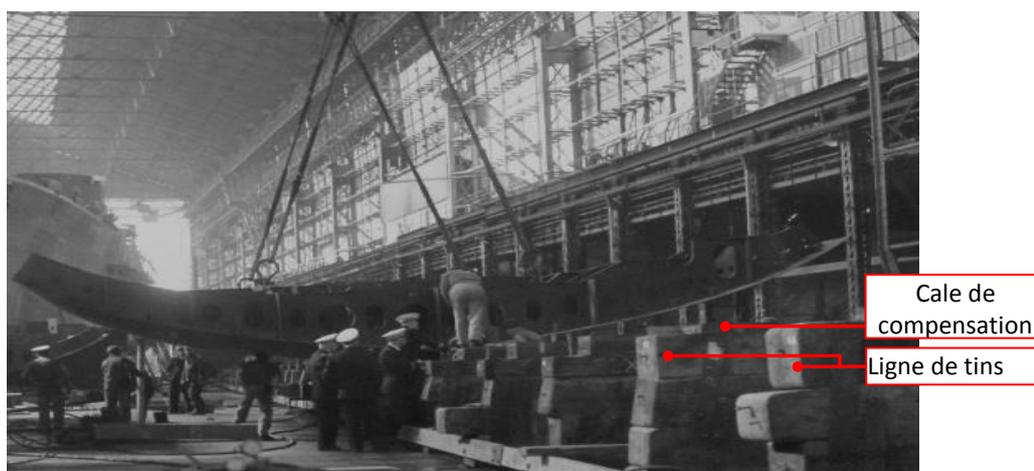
Mise sur tins d'un bloc de fond d'un escorteur
